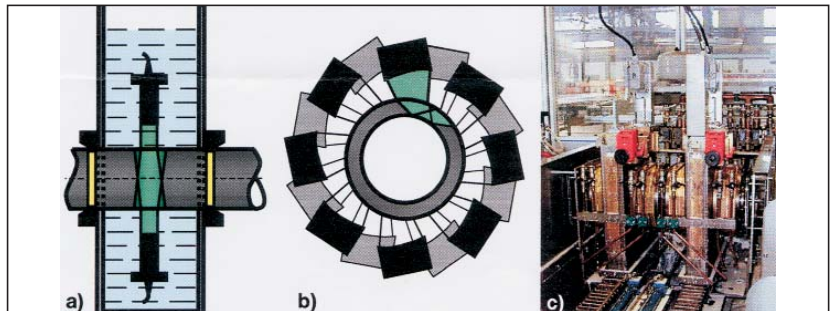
Das Prinzip der Tauchtechnik (Prüfköpfe und Prüfgut unter Wasser) wird erfolgreich für die rotationslose Prüfung von Langprofilen eingesetzt, b) mögliche Anordnung der Winkelprüfköpfe für die Rohrprüfung, c) HRP-Mechanik für Stangenprüfung
